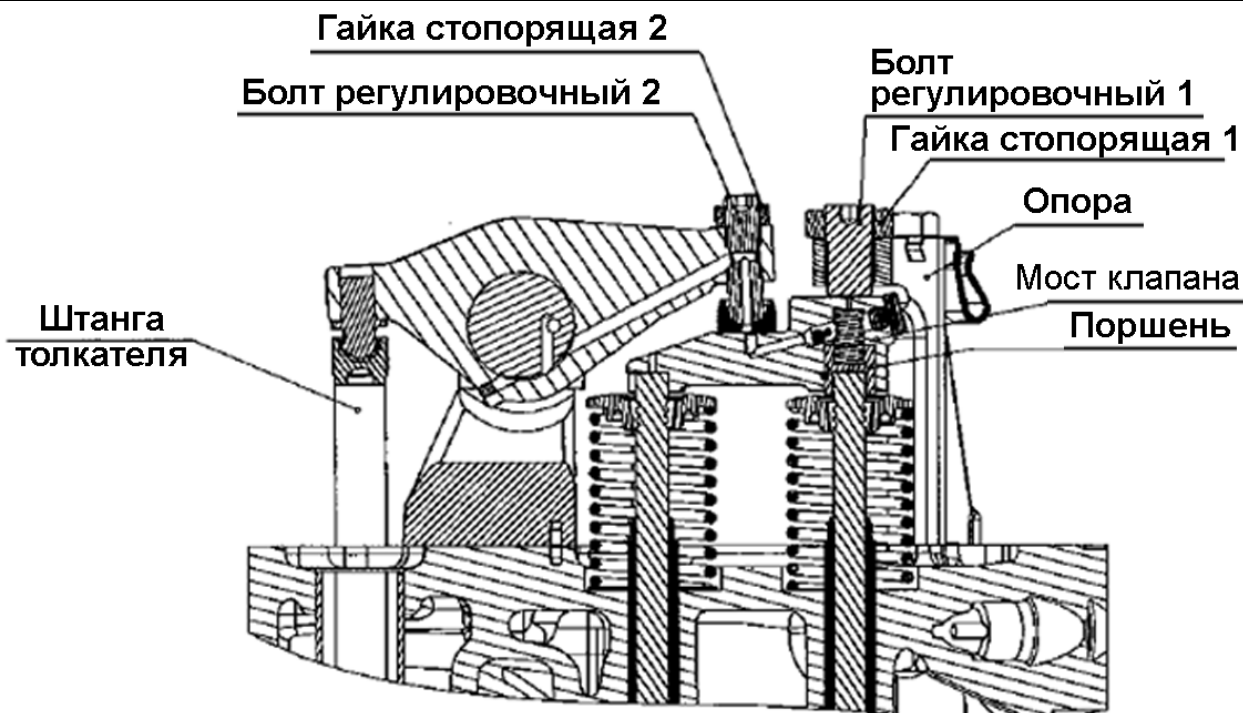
Выпускной клапан и регулировка зазора EVB
